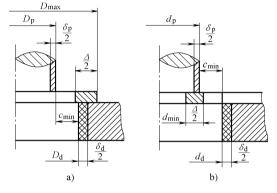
冲裁模刃口尺寸与公差位置 a) 落料 b) 冲孔
